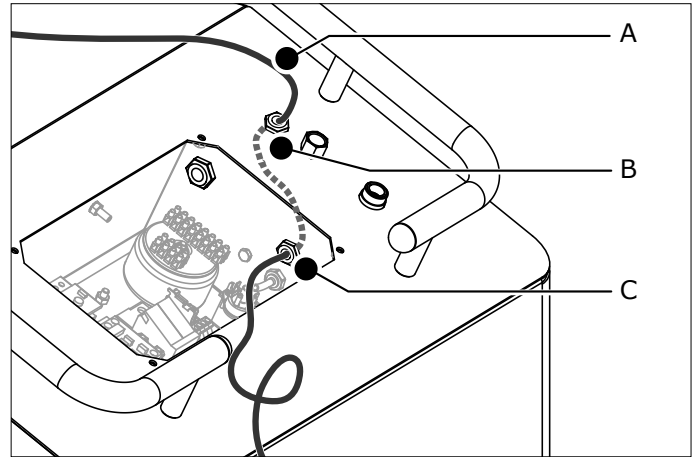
Collegamento del cavo della lampada di lavoro
